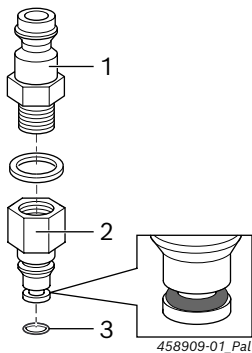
Montagem do adaptador de retorno 1 687 016 138
